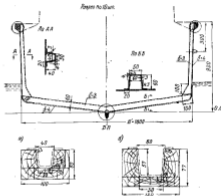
Конструктивный макет шпангоут моторкера длиной 7,5 м с пустотелыми шпангоутами: а — конструкция борта для изготовления бортовой обшивки; б — конструкция борта для изготовления днищевой обшивки.
